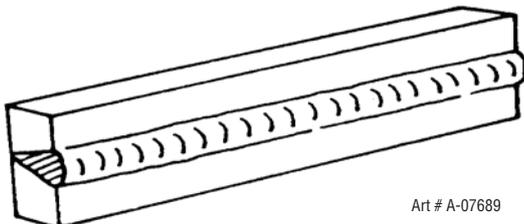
Position horizontale, soudure par aboutement
